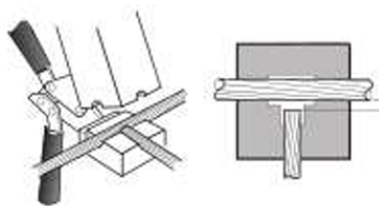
Introducir en el molde los cables a soldar según se muestra en la figura.
